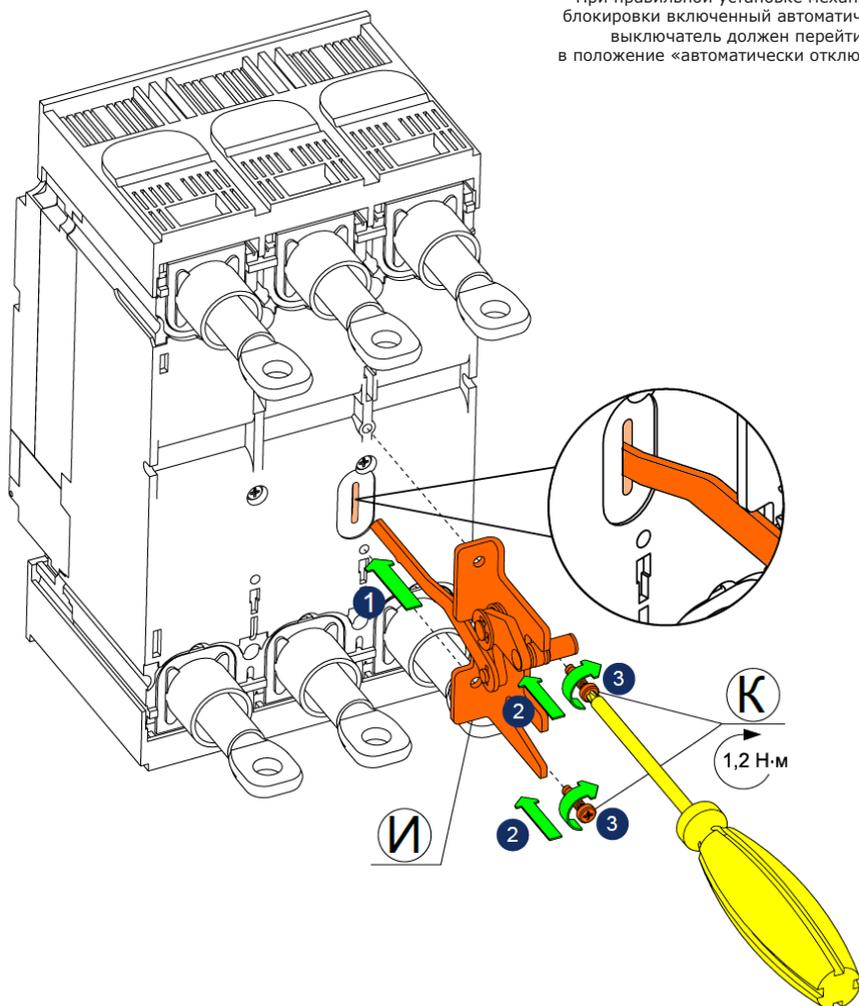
Установка механизма блокировки на стационарный выключатель
